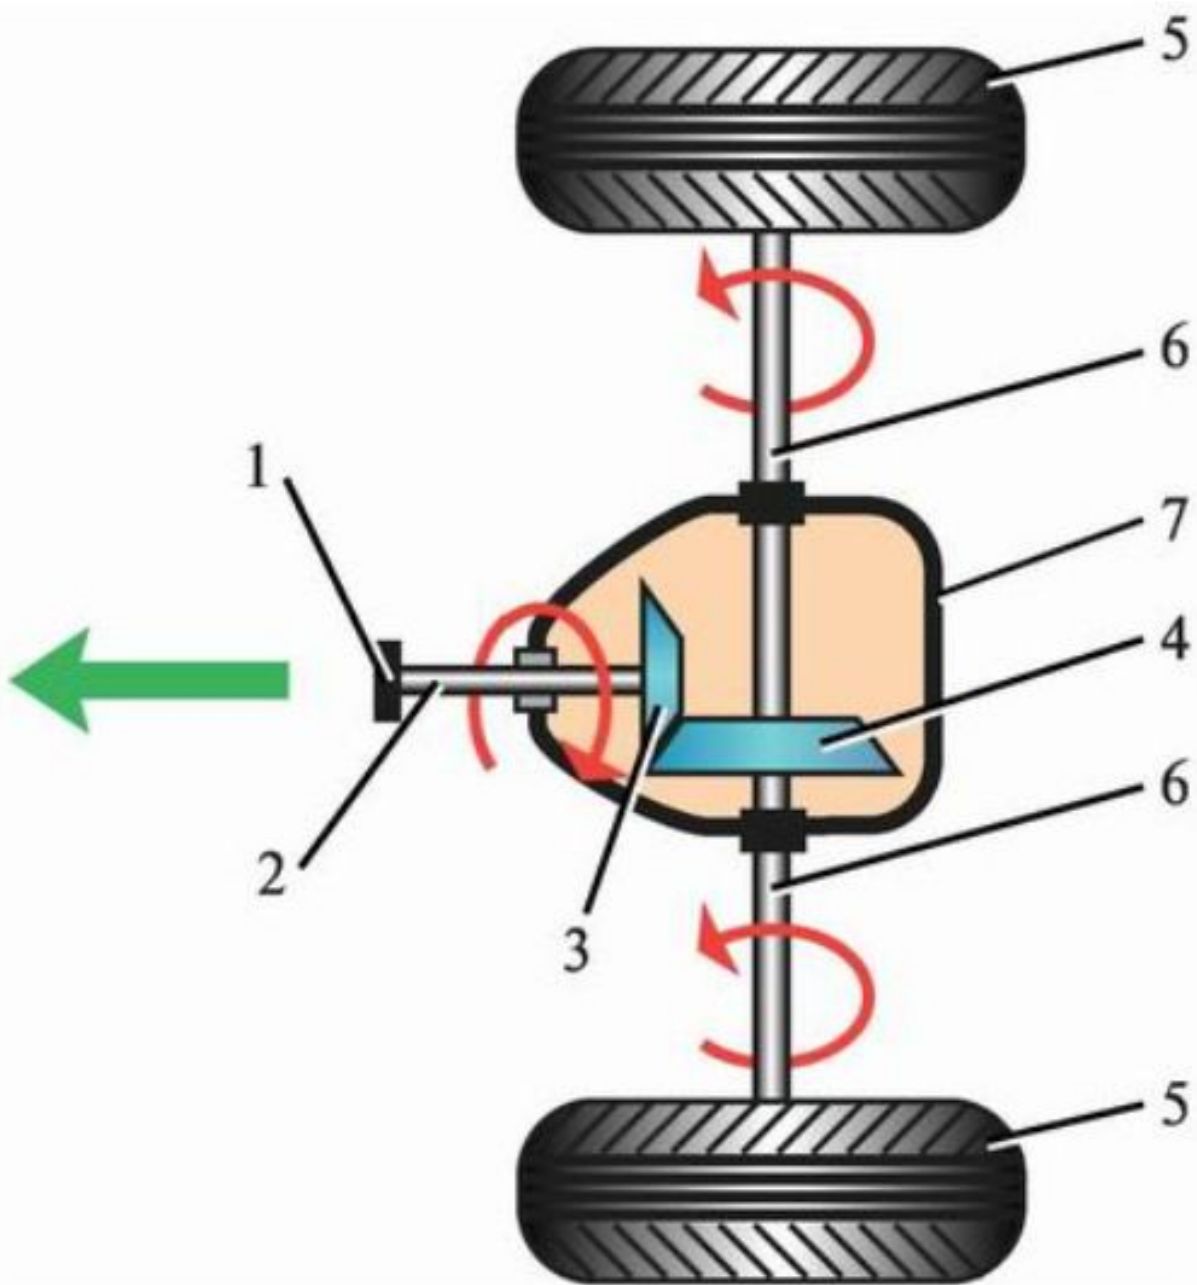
Схема работы главной передачи: 1 – фланец; 2 – вал ведущей шестерни; 3 – ведущая шестерня; 4 – ведомая шестерня; 5 – ведущие (задние) колеса; 6 – полуоси; 7 – картер главной передачи
